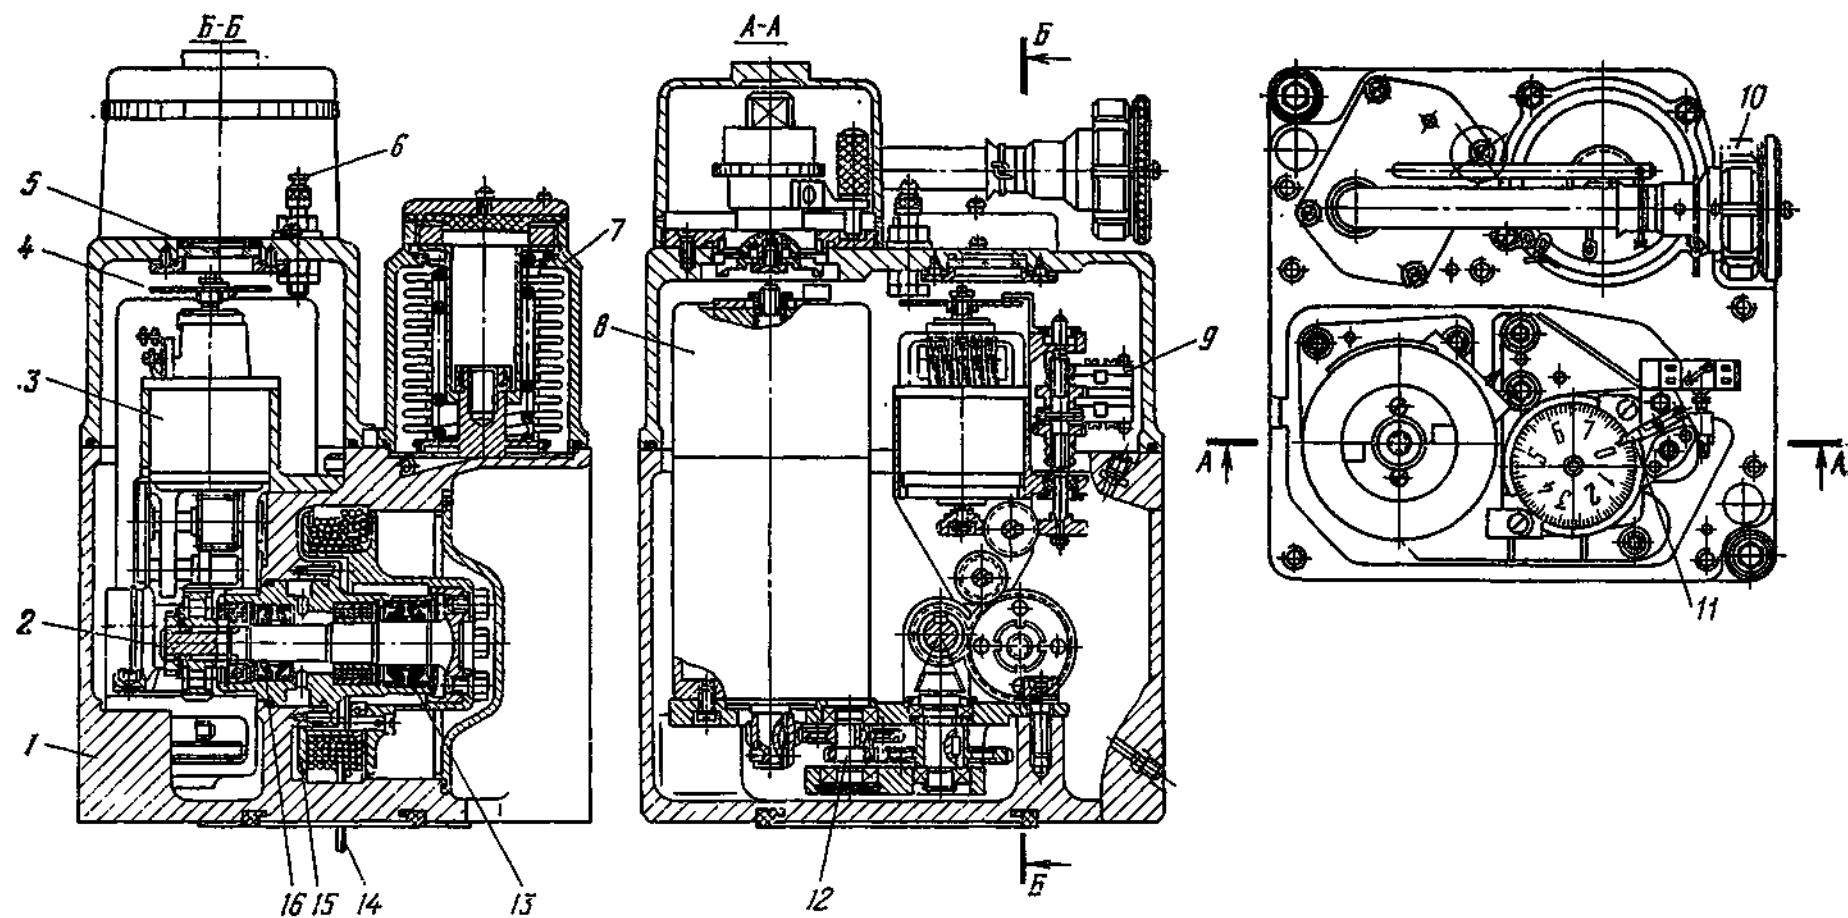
Конструкция привода СУЗ РР-А3 реактора РБМК
